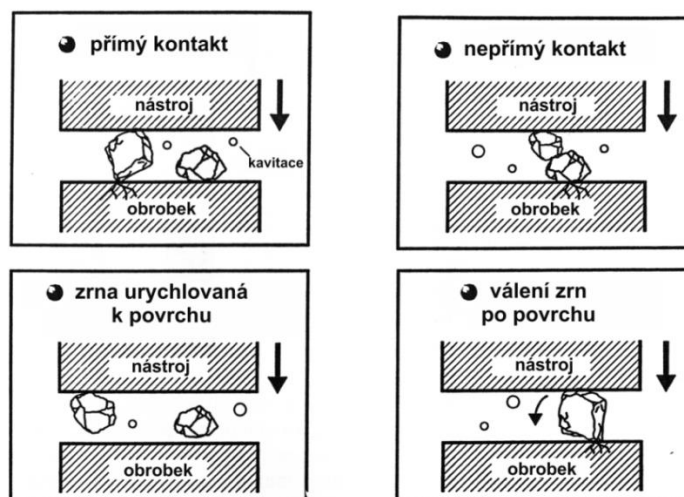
Princip stroje pro obrábění ultrazvukem [9]
